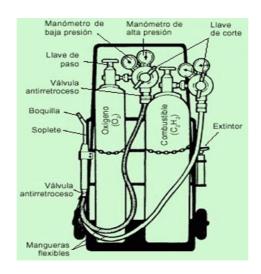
Elementos principales de una instalación móvil de soldadura por gas
